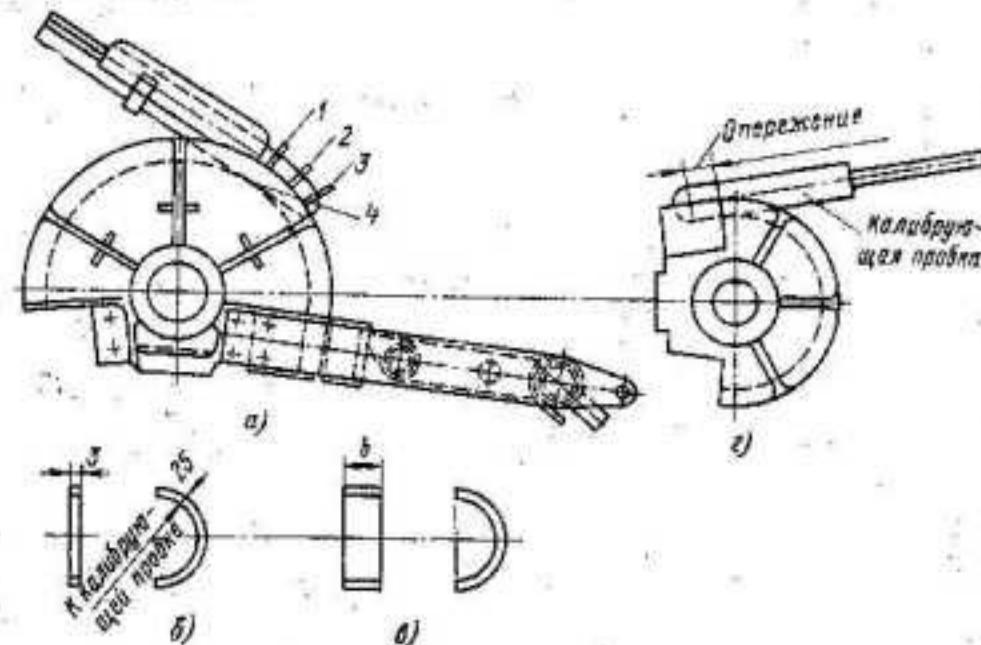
Установка калибрующей пробки по установочному шаблону.
